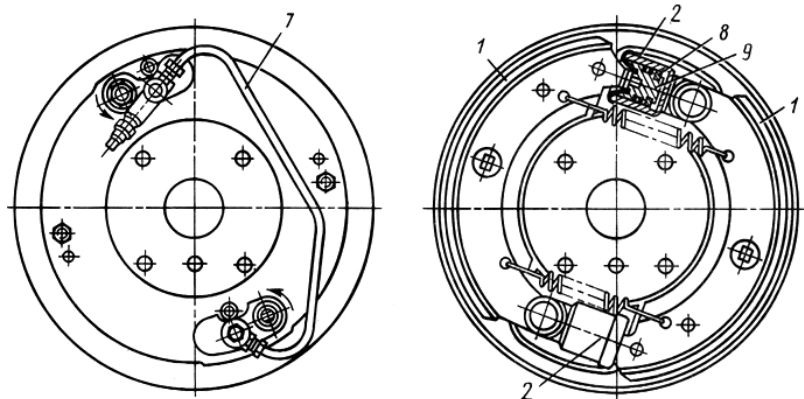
Конструкция барабанного тормозного механизма с гидравлическим приводом, равными приводными силами и двухсторонним расположением фиксированных опор: 1 — тормозные колодки; 2 — колесный цилиндр; 7 — соединительная трубка; 8 — разрезное упорное кольцо; 9 — поршень
